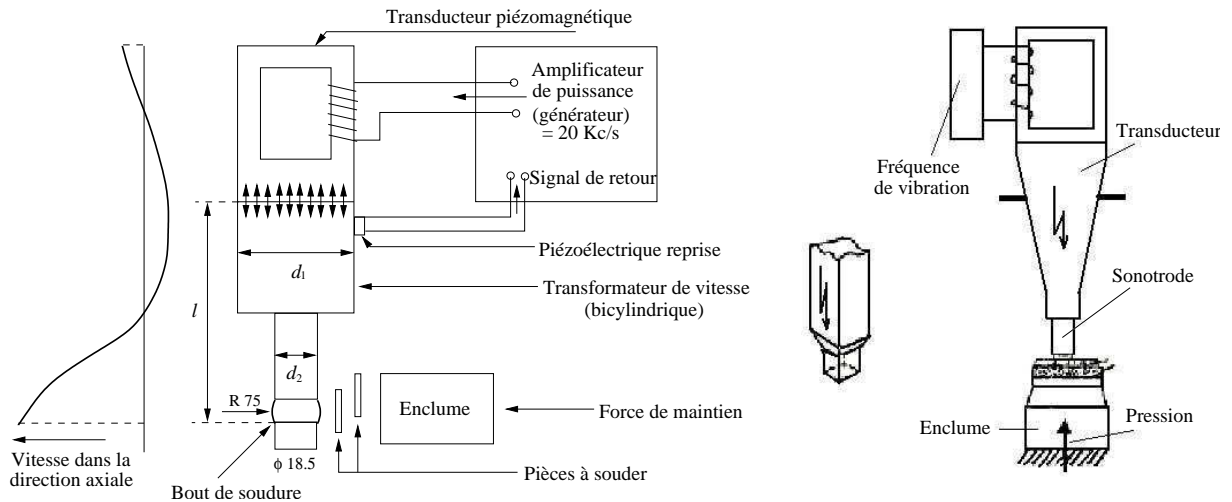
Ensemble acoustique pour deux techniques de soudage : pour les métaux (gauche) [3, 7] et pour les plastiques (droite) [8]
